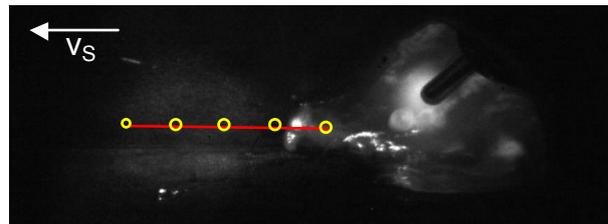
Einzelbild aus einer CPC-Aufnahmesequenz beim Laser-MSG-Hybridprozess, synchronisiert mit den Strompulsen der Schweißstromquelle – Die rote Verbindungslinie mit den gelben Stützstellen zeigt die erfasste Fuge (Quelle: Fraunhofer Institut für Lasertechnik)
